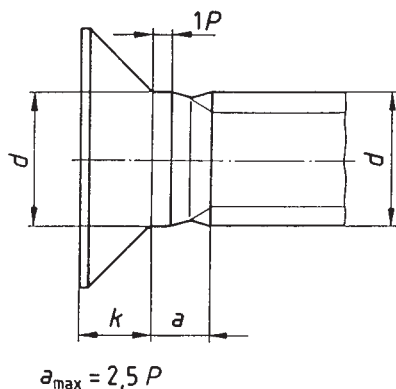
Schrauben mit zylindrischem Ansatz unter Kopf
